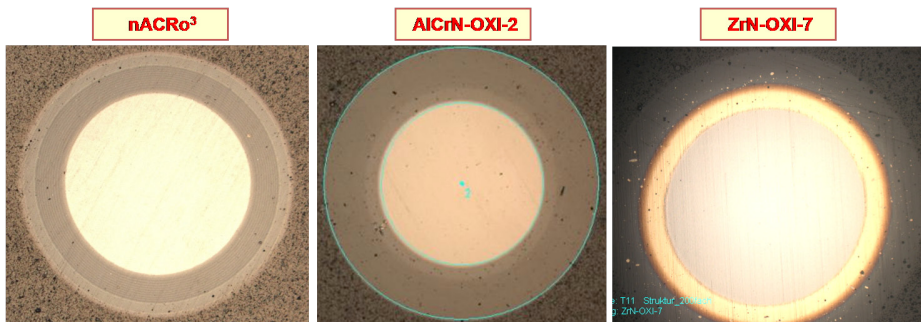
Schichtsysteme für die Beschichtung der Fräser
